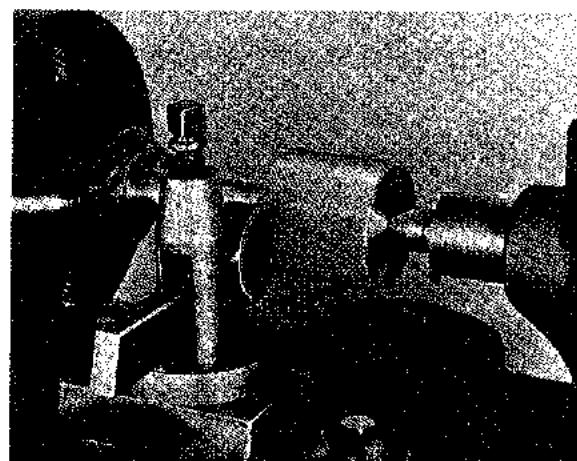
Grafilado de una pieza en el torno (South Bend Lathe Works).
